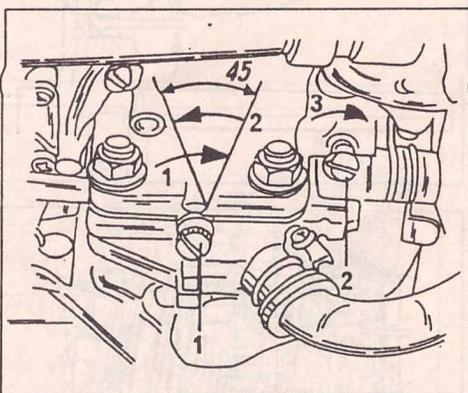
Расположение винта регулировки качества смеси (1) и винта регулировки холостого хода (2). Стрелки и цифры вверх рисунка указывают на порядок регулировки.
